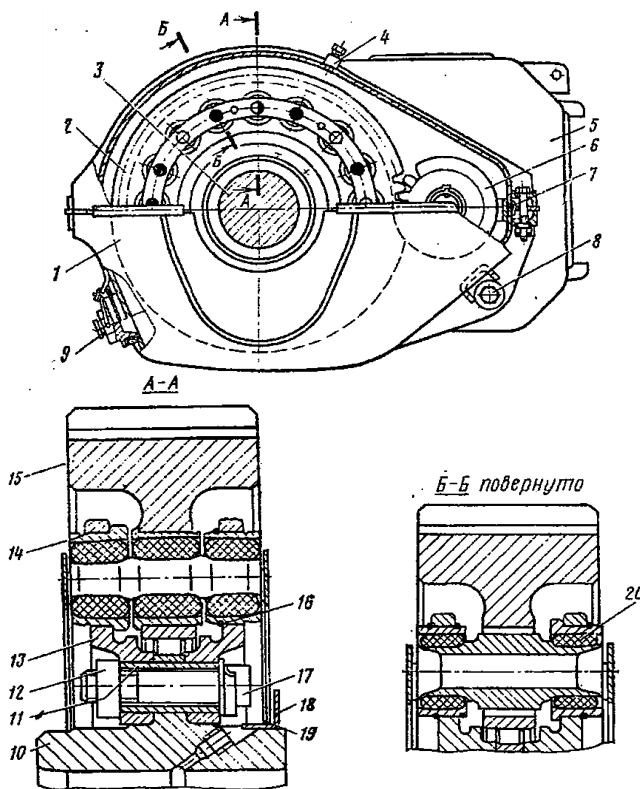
Пружне зубчасте колесо тягового редуктора тепловоза 2ТЭ116
